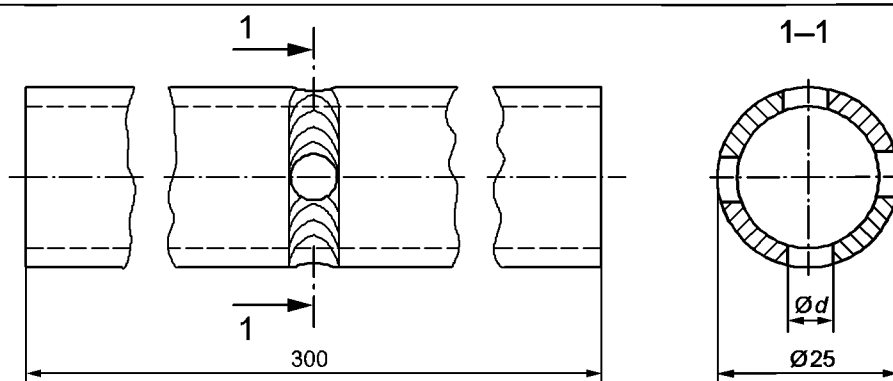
Контрольная длина и положение образцов для испытаний на изгиб или излом стыкового шва труб
